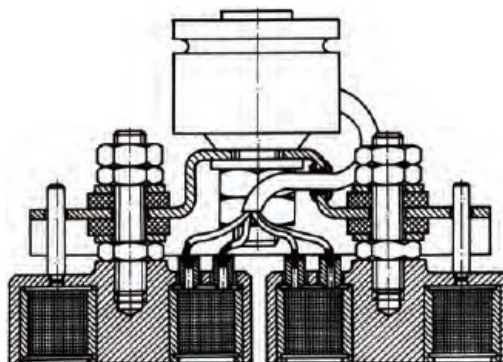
Pasivní magnetický efektor s pneumatiky pro odejmutí objektu manipulace [37]
